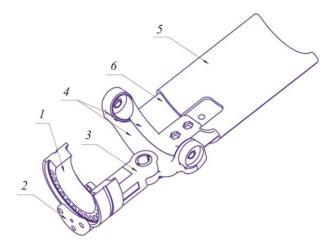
Эскиз устройства тренажера для реабилитации локтевого сустава: I — поворотная дуга, совершающая вращательное движение вокруг своей оси (образует пару V класса); 2 — регулируемая опора поворотной дуги; 3 — поворотный рычаг, в котором установлена опора 2; 4 — кинематическая пара, служащая для сгибания-разгибания локтевого сустава; 5 — неподвижная часть ложемента для плеча; 6 — регулируемая часть ложемента, образующая поступательную пару в процессе настройки тренажера с неподвижной частью
